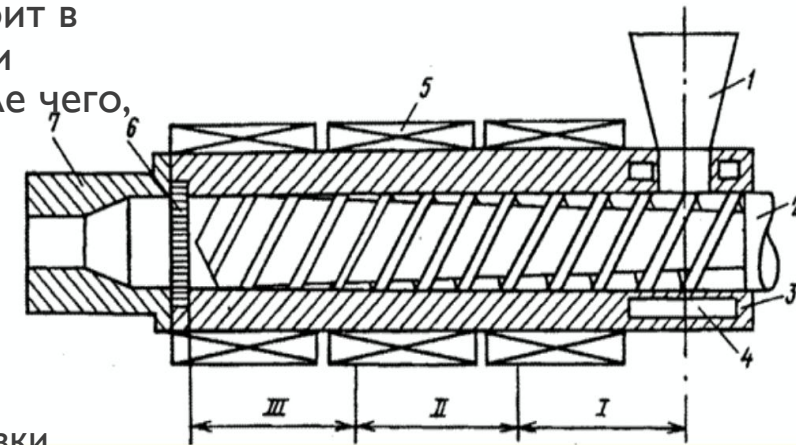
Схема одношнекового экструдера: 1- бункер; 2- шнек; 3- цилиндр; 4- полость для циркуляции воды; 5- нагреватель; 6- решетка с сетками; 7- формующая головка.
